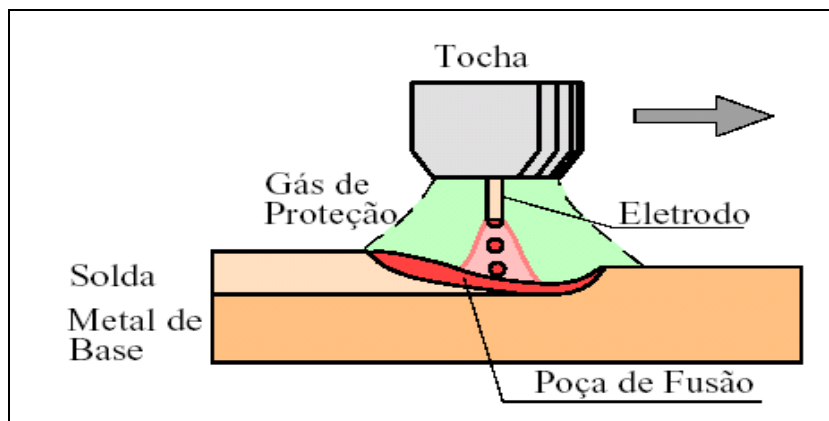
Processo de soldagem MIG/MAG (Fonte: Marques^[22])
